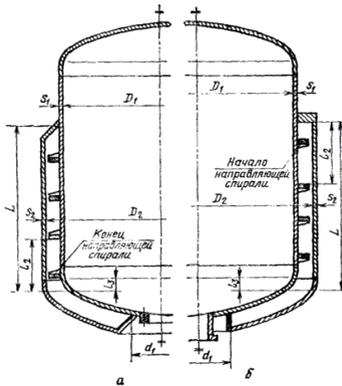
Рубашка реактора с приварными ребрами
